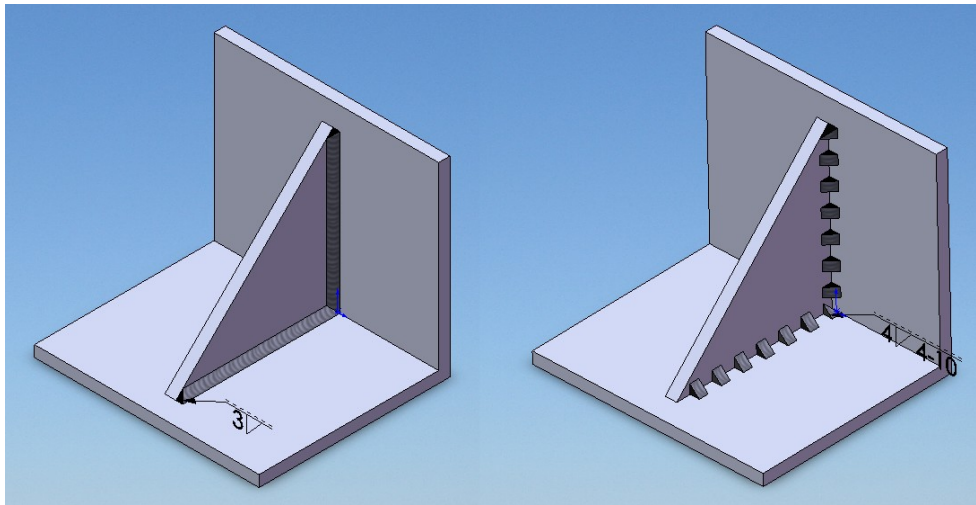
Ejemplo de la operación Cartela y Cordón de Soldadura Continuo e Intermitente
